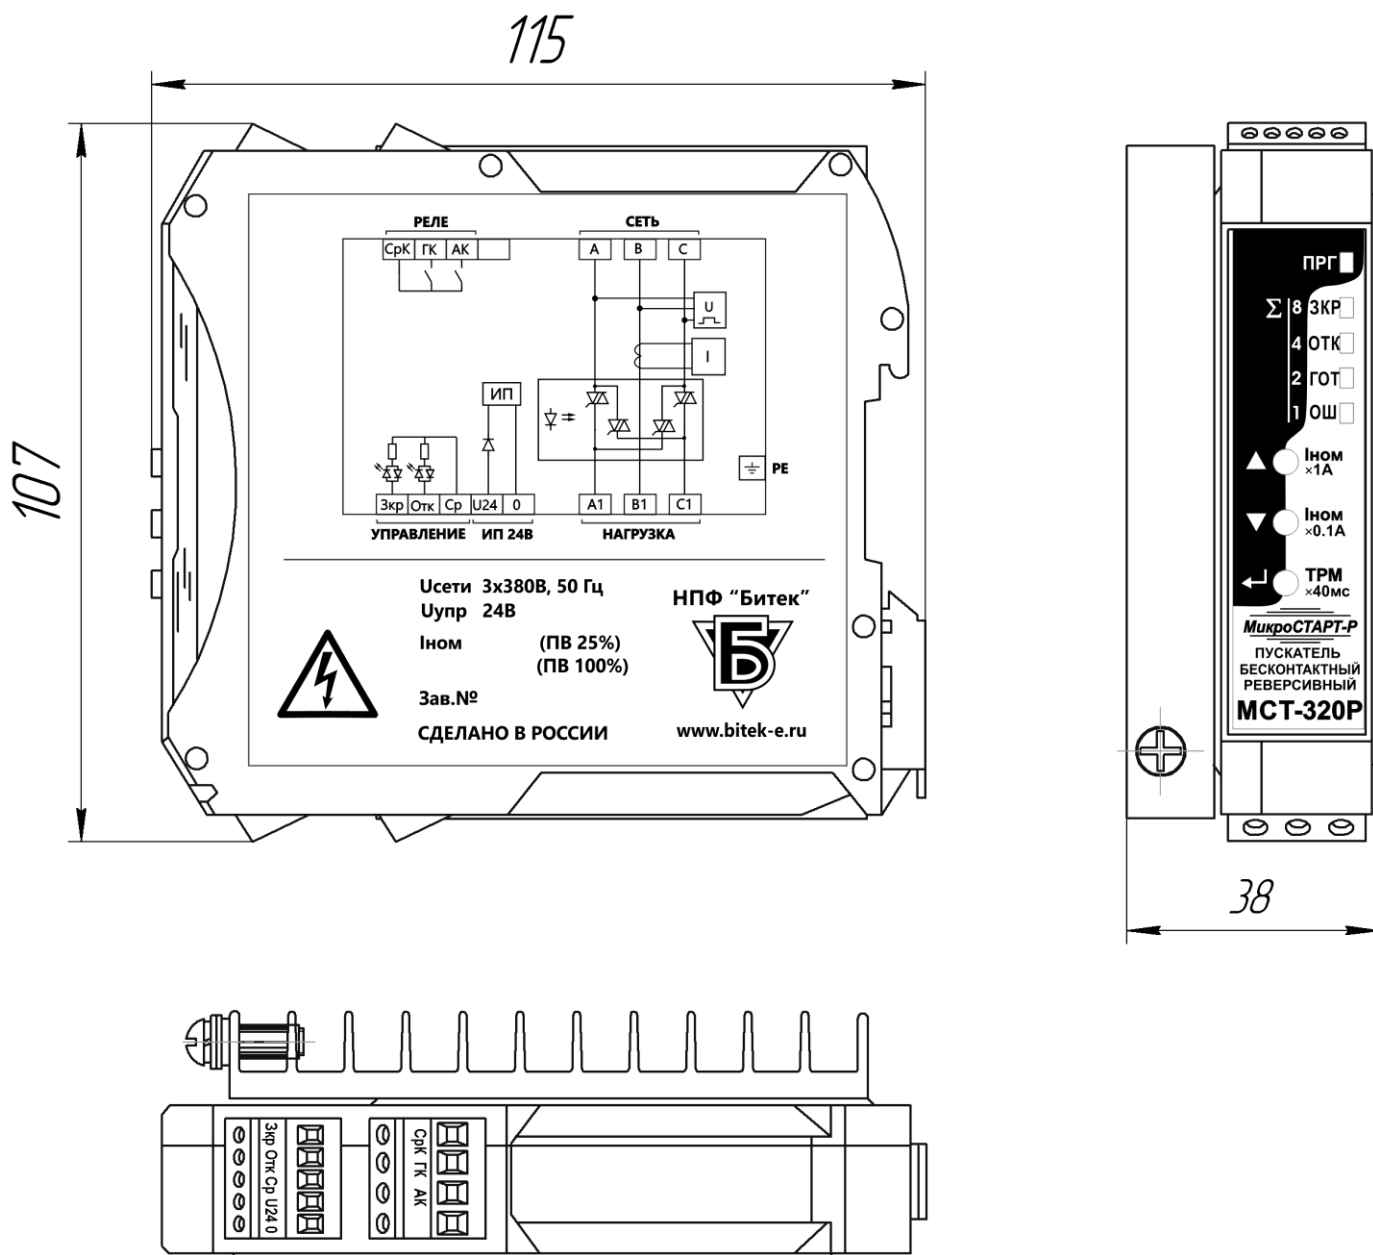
Габаритно-установочные размеры МСТ-320Р, МСТ-420Р
